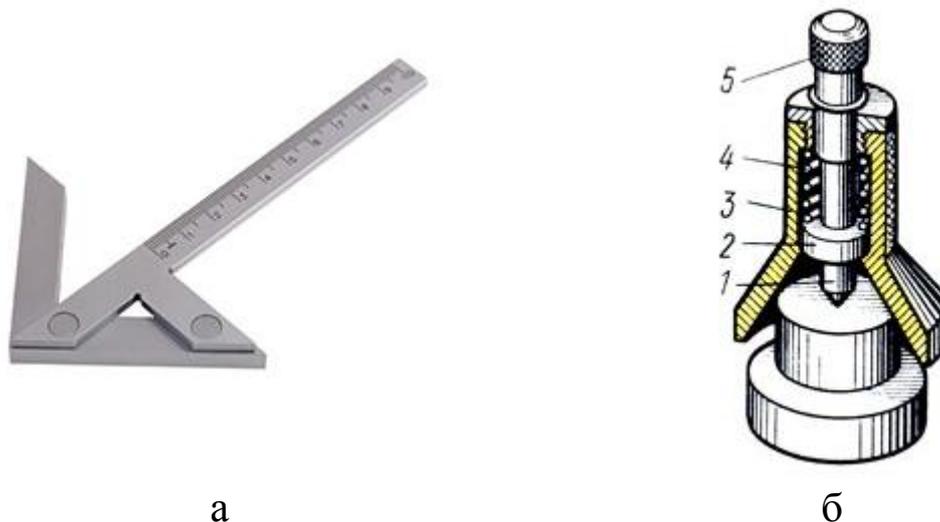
Инструмент для нахождения центров деталей: а – центроискатель; б - кернер-центроискатель: 1 - кернер, 2 - фланец, 3 - колокол, 4 - пружина, 5 - головка
